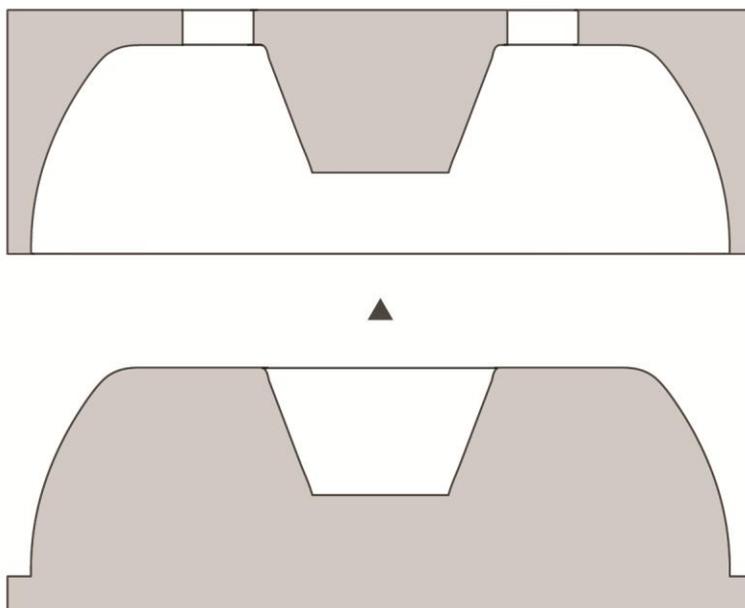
Corte esquemático de modelo e molde do corpo externo da panela
